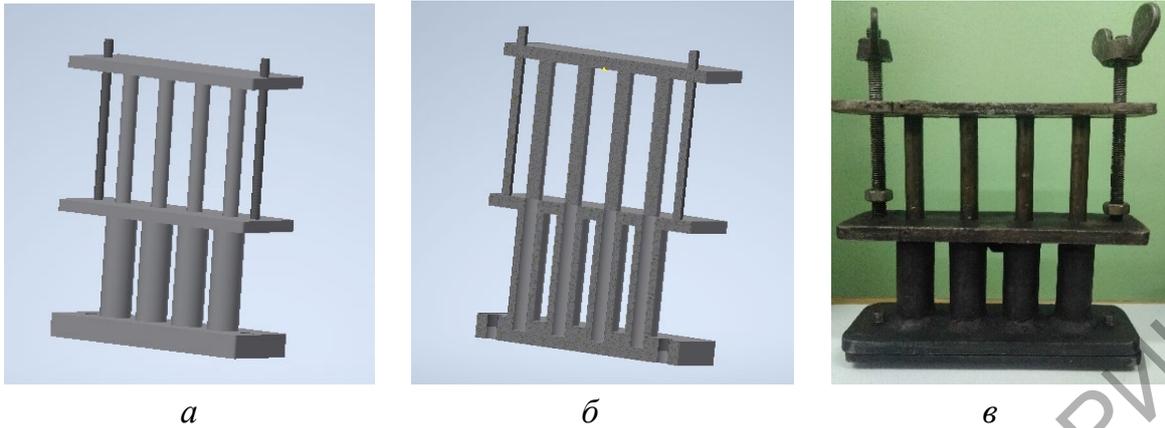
Пресс для изготовления экспериментальных образцов:
